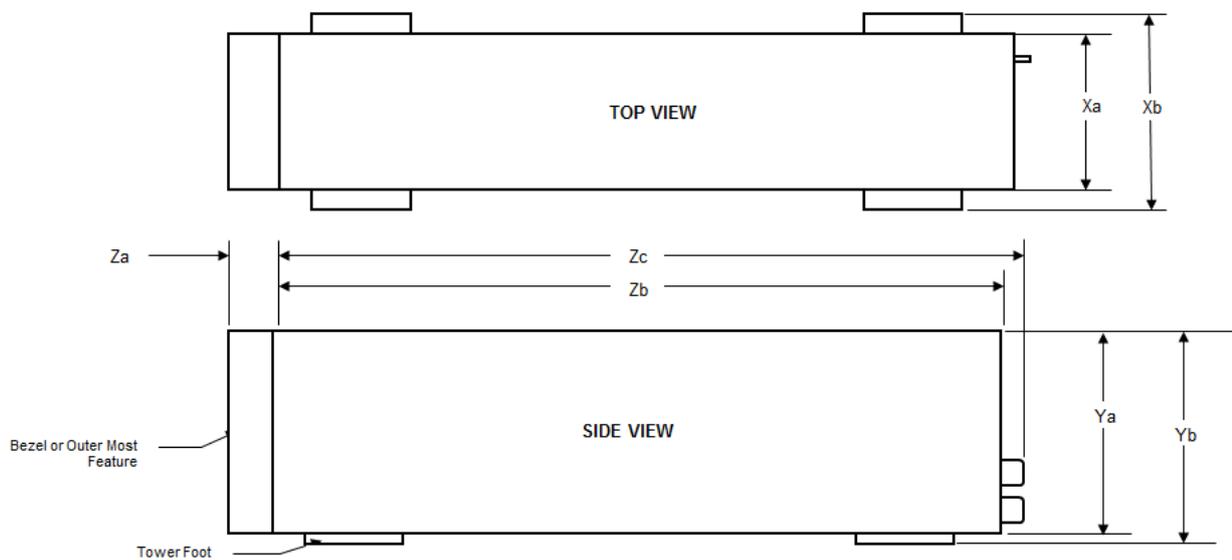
PowerEdge T150 – Gehäuseabmessungen
